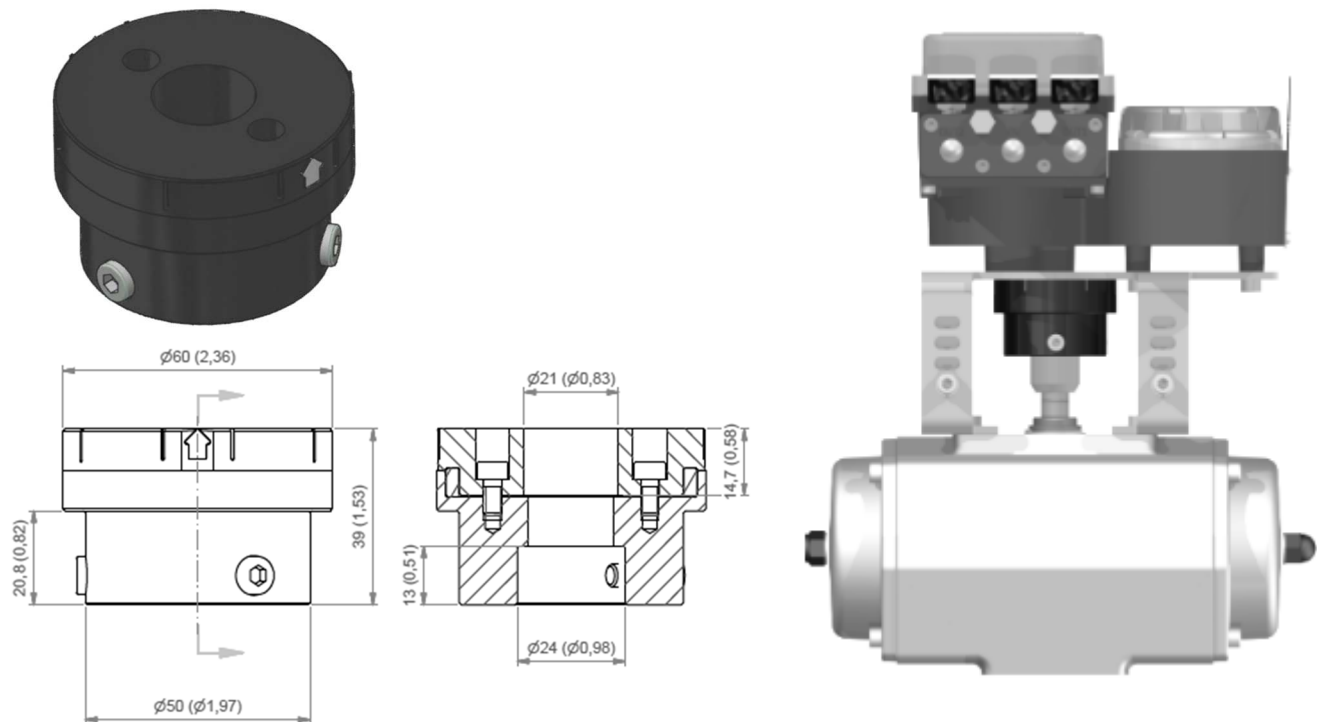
Dimensional e montagem do ímã rotativo.
